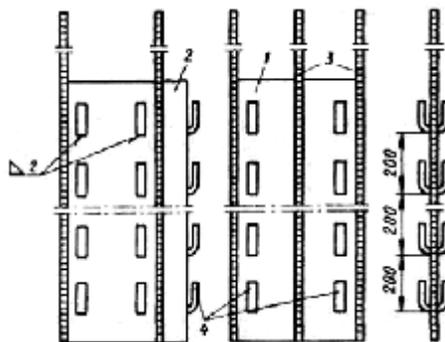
Схема сборки заготовок под ЭШС на трех опорах:
